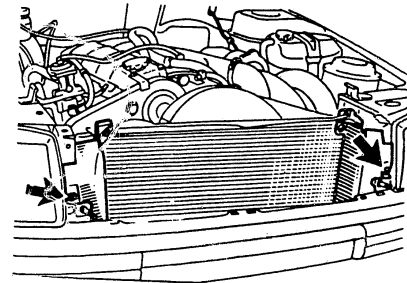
Motorausbau: Der Kühler ist mitsamt den seitlichen Leitblechen zu entfernen. Der Stossfänger muss nicht demontiert werden.
